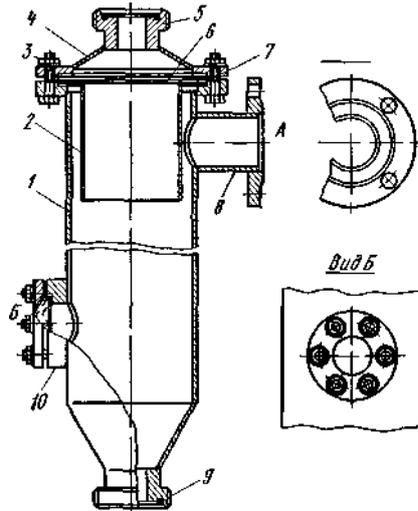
Схема нагревателя инфузионного типа («молоко в пар») со струйными форсунками: 1 — камера нагревания; 2 — отбойник пара; 3 — болтовое соединение; 4 — крышка; 5 — патрубок для ввода молока; 6 — струе образующий диск, 7 — уплотнительные прокладки, 8 — патрубок для ввода пара, 9 — патрубок для вывода стерилизованного молока; 10 — смотровое окно
